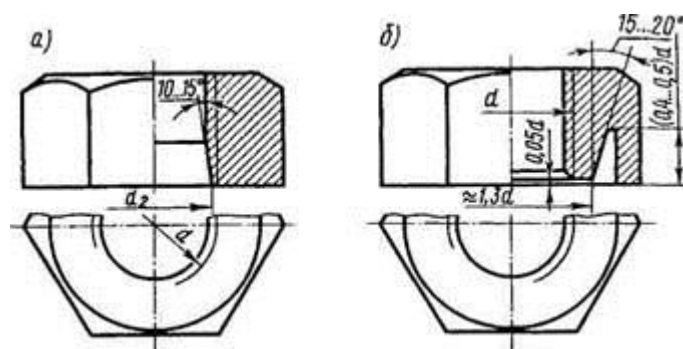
Конструкции гаек для выравнивания сил по виткам резьбы: а — гайка с поднутрением; б—гайка с конической выточкой
